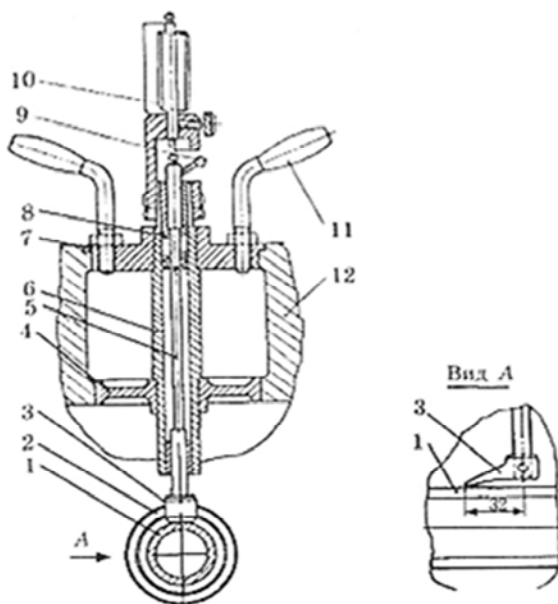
Приспособление для проверки перпендикулярности оси цилиндра к оси коленчатого вала двигателя:
